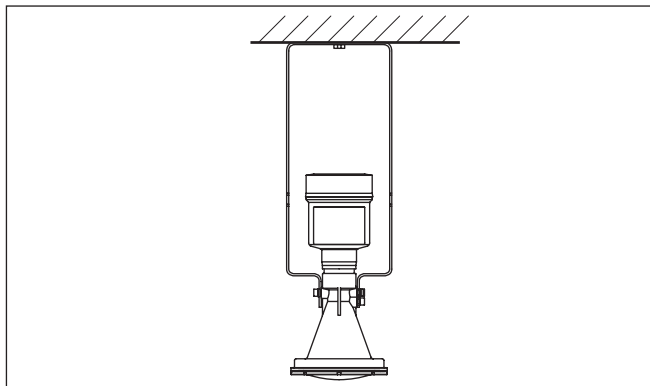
Монтаж на перекрытии на монтажной скобе длиной 300 мм
